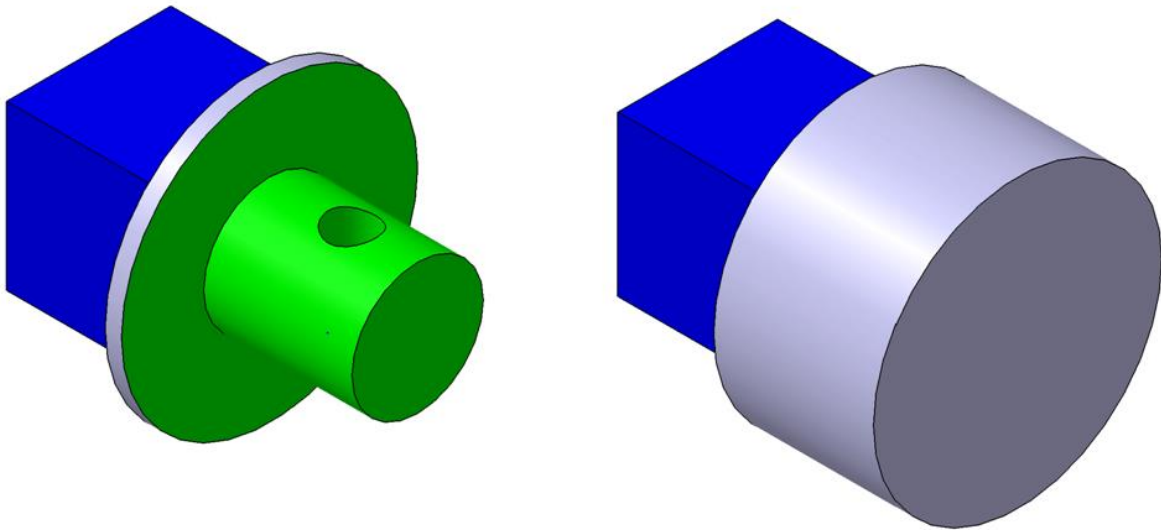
Testwerkstück für Fräsmaschinen nach Brillinger M.
